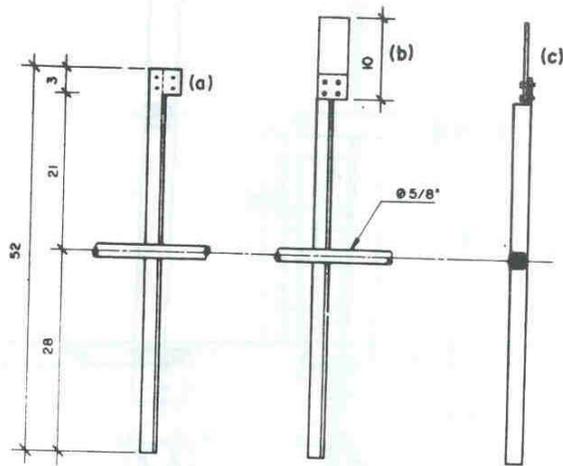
Vista frontal do braço impulsor (a) com detalhe de fixação da borracha flexível (b) e vista lateral (c).
